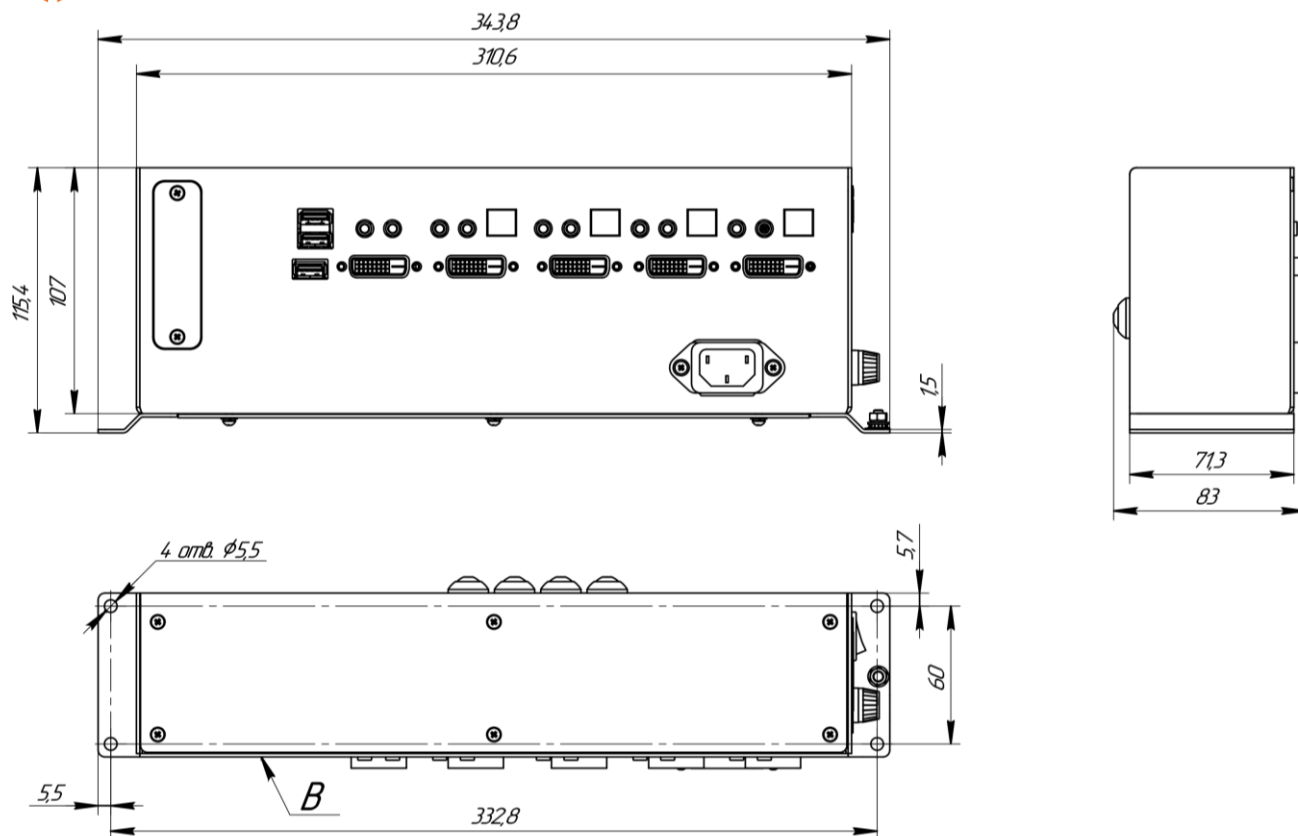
Габаритные размеры КУВВ-143-104
